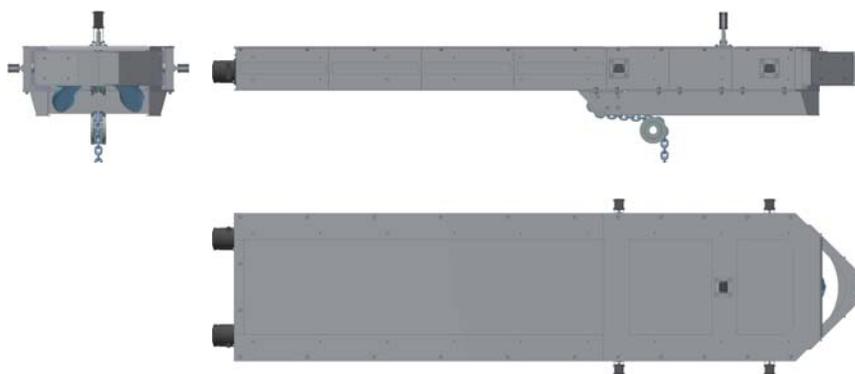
Ankerlade mit eingefahrener Lade (Vorder-, Seiten- und Grundansicht)
